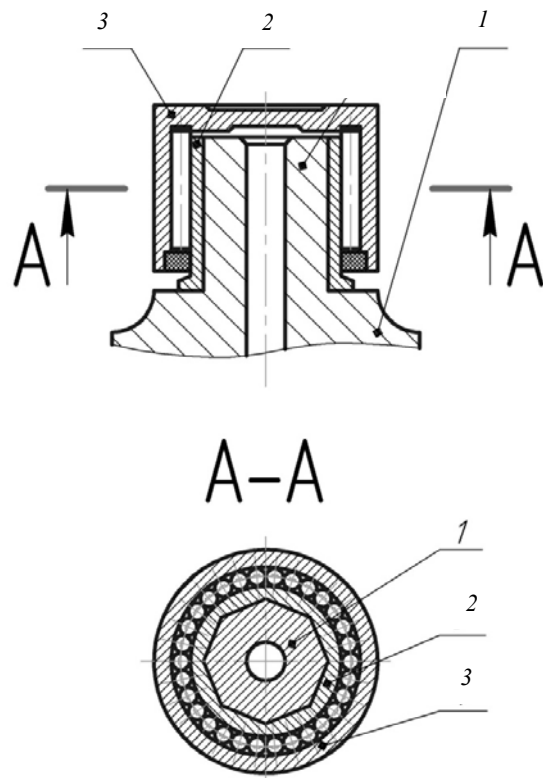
Карданный шарнир с втулками из материала высокой твердости
